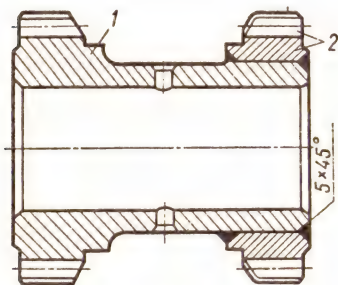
Восстановление блока шестерен заднего хода коробки передач постановкой зубчатого венца:
